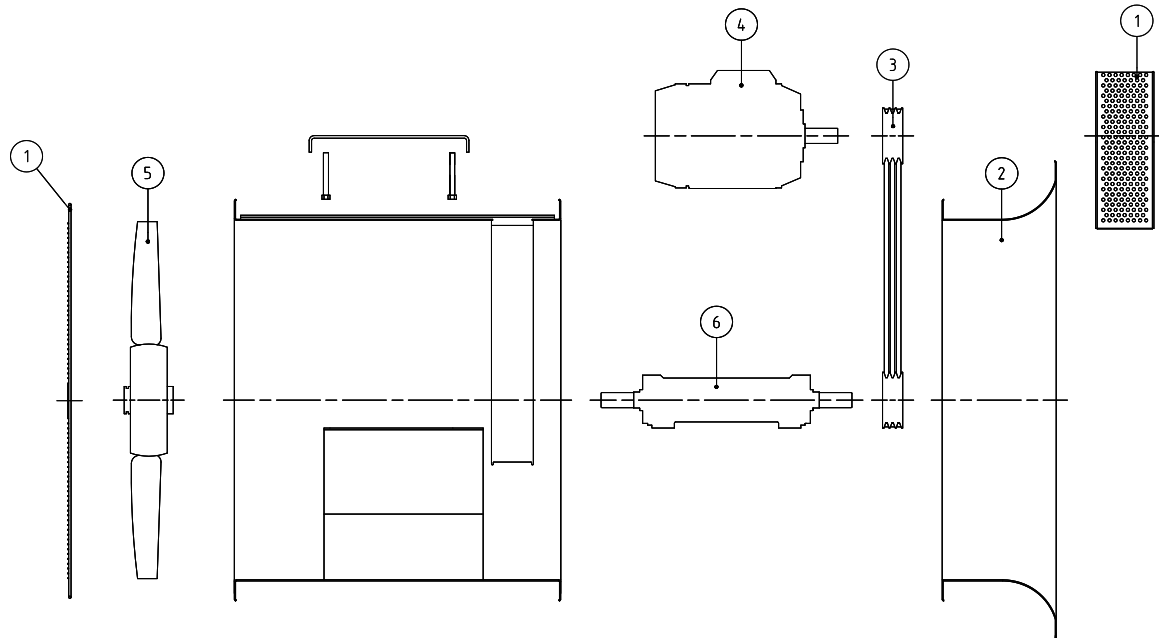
Explosionszeichnung des Ventilators in Ausführung 9
